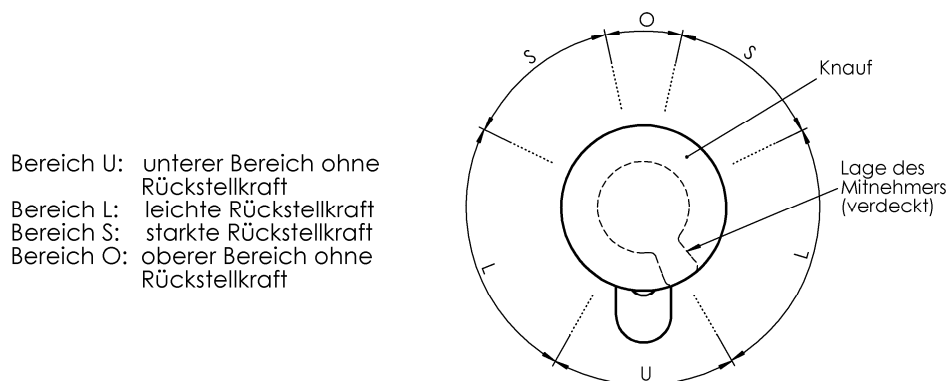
Verschiedene Positionen des Schließbarts beim AP Zylinder
